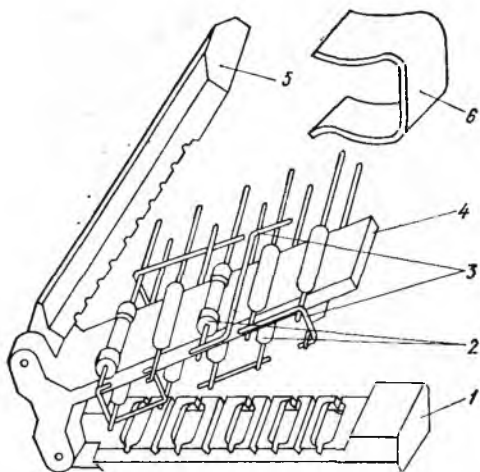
Приспособление для рельефно-точечной конденсаторной микросварки модулей.
